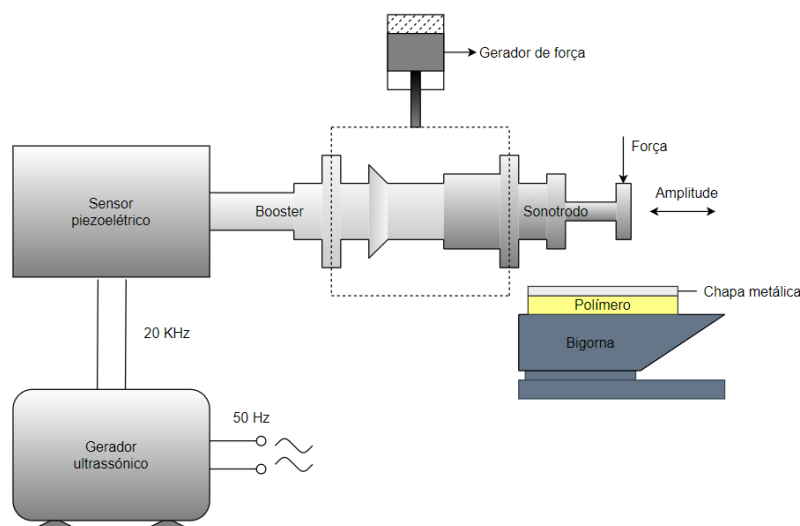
Soldadura por ultrassons. Adaptado de [34].
